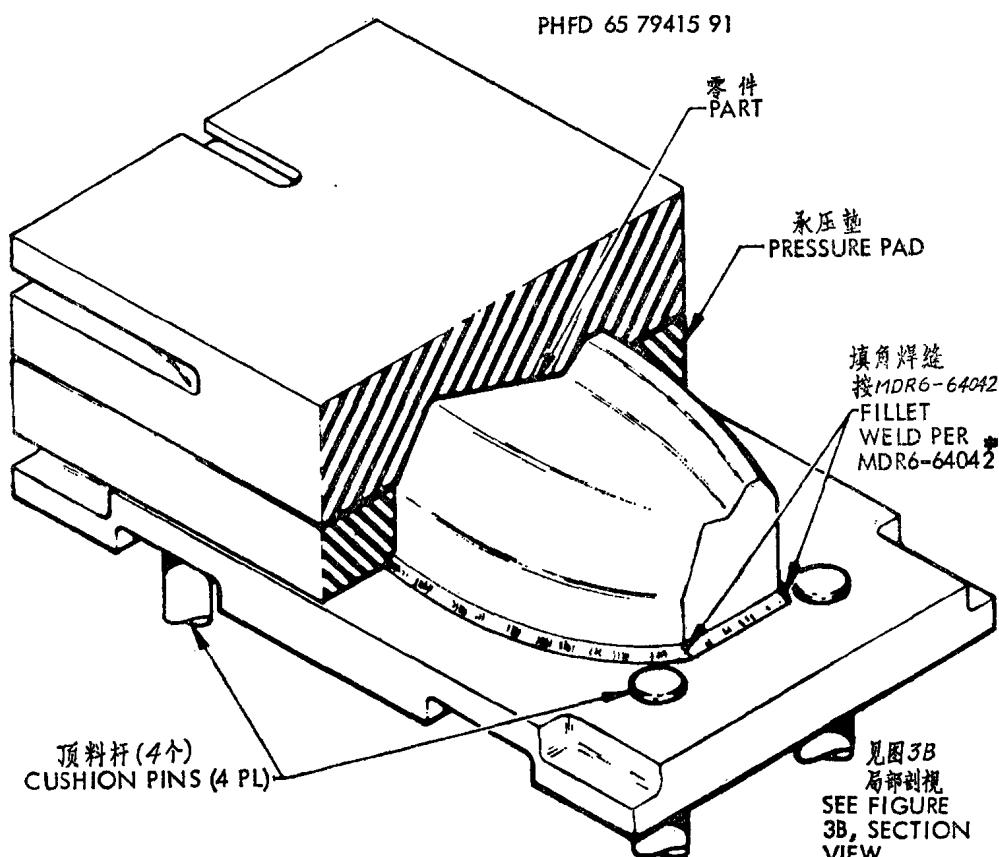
A 典型焊接模结构——材料为INCOLOY802
